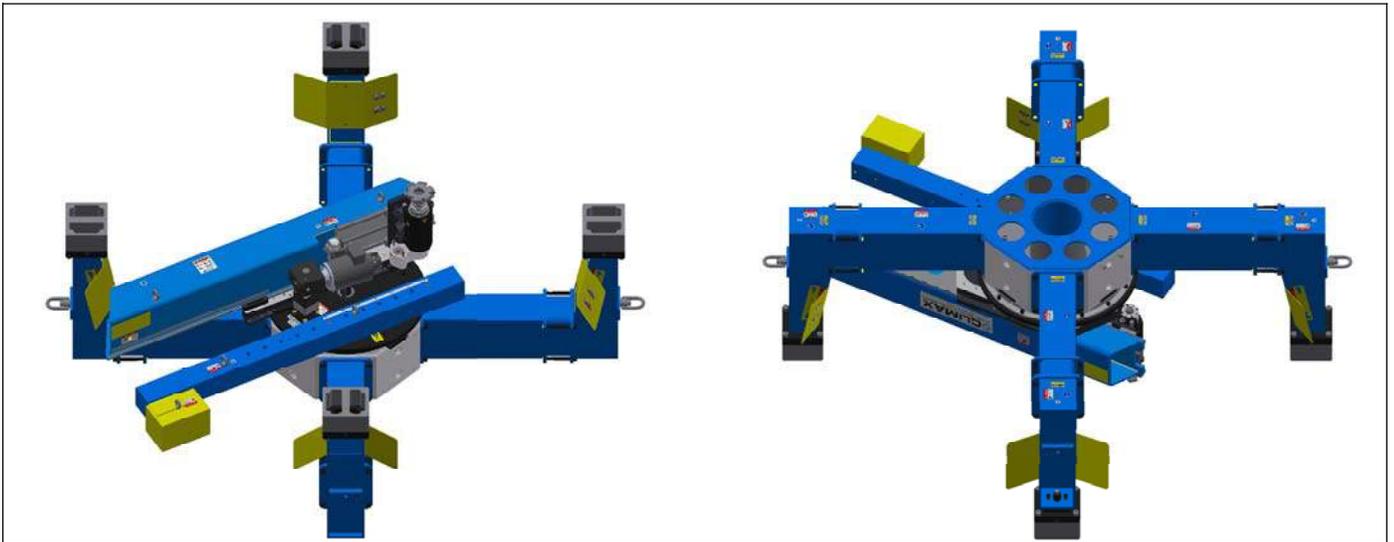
ENSEMBLE BLOC ÉLÉVATEUR ET JAMBE
